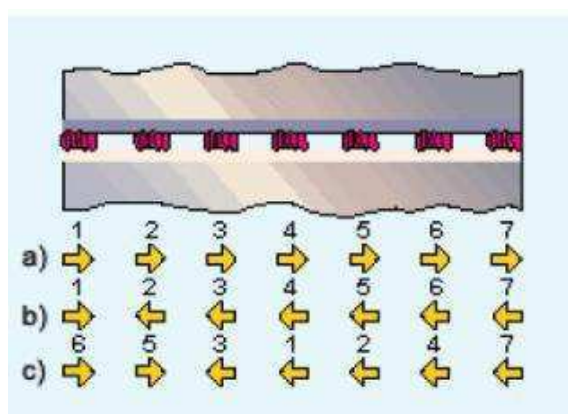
Técnicas de fixação por ponto de solda. (TWI,2014).
